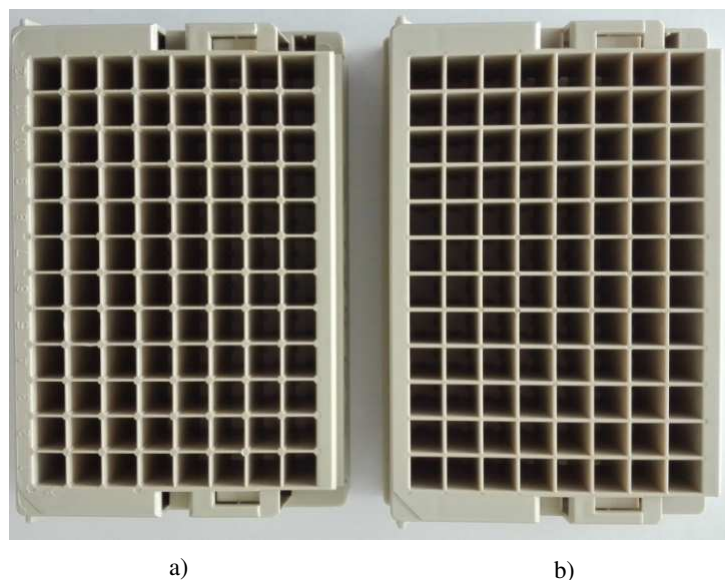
Lado da extração da peça *Support*: molde de fabrico convencional (a); molde de fabrico aditivo (b)
